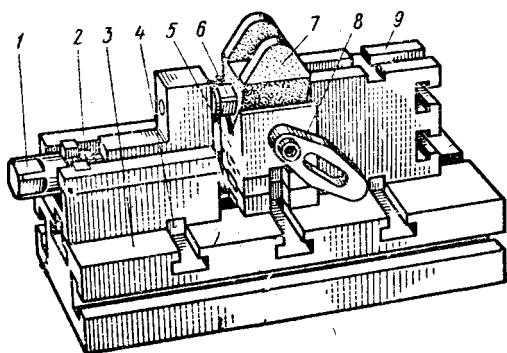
Универсально-сборное приспособление для крепления вилок при фрезеровании
